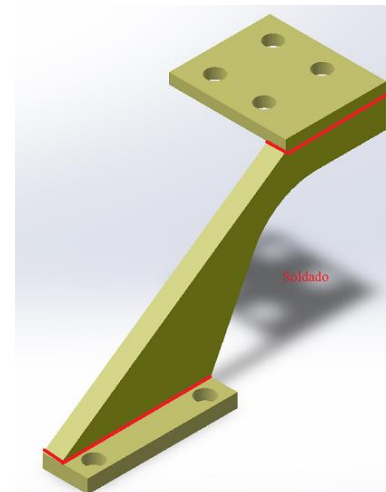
Vista de soldado de pieza N°6 (Fuente 92)
